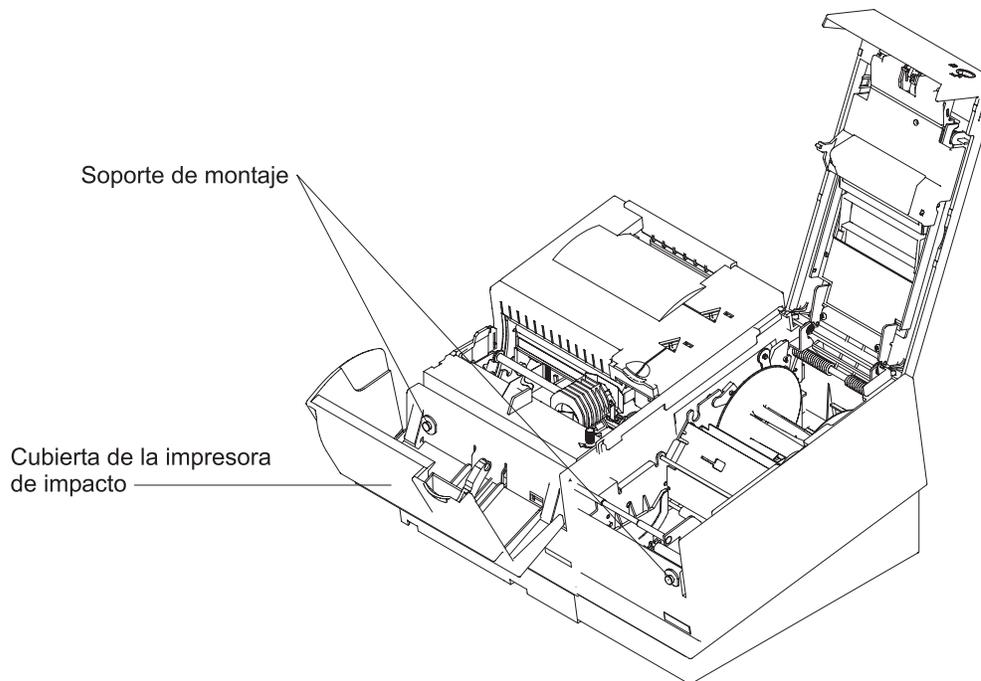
Soportes de montaje en el lado frontal de la cubierta base
